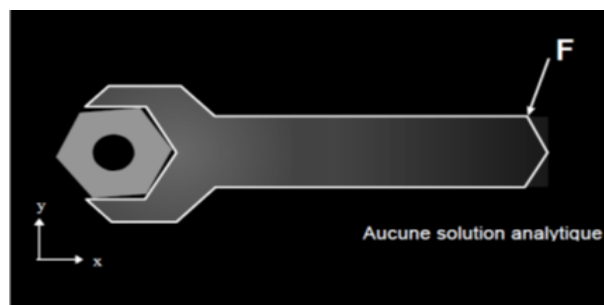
Llave de mano problema complejo, para el análisis de la ingeniería aplicada.
